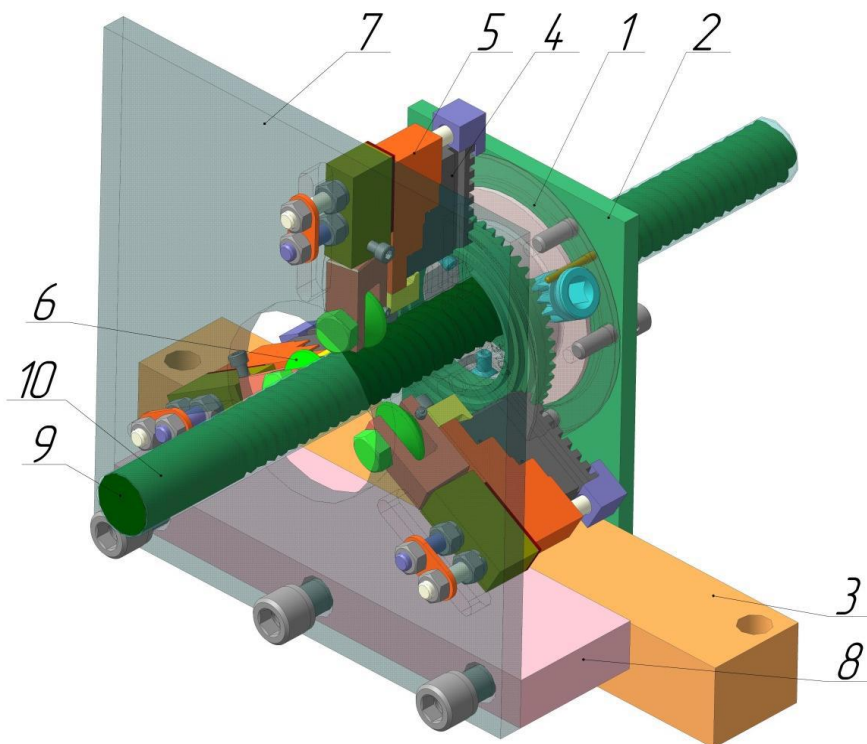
Обкатна головка (3D-модель): 1 –патрон трикулачковий, 2 – плита опорна, 3 – опора, 4 – кулачок, 5 – головка обкатна, 6 – ролик, 7 – плита зміцнювальна, 8 – плита утримуюча, 9 – оправка, 10 – труба-заготовка
